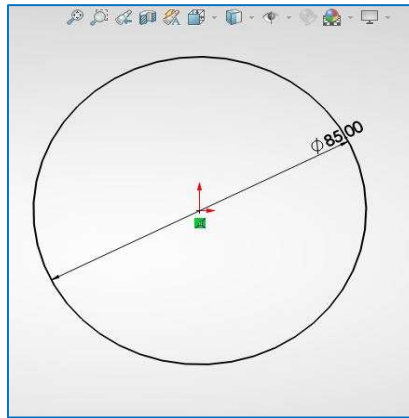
Étape de la construction d'une forme 2D du piston
